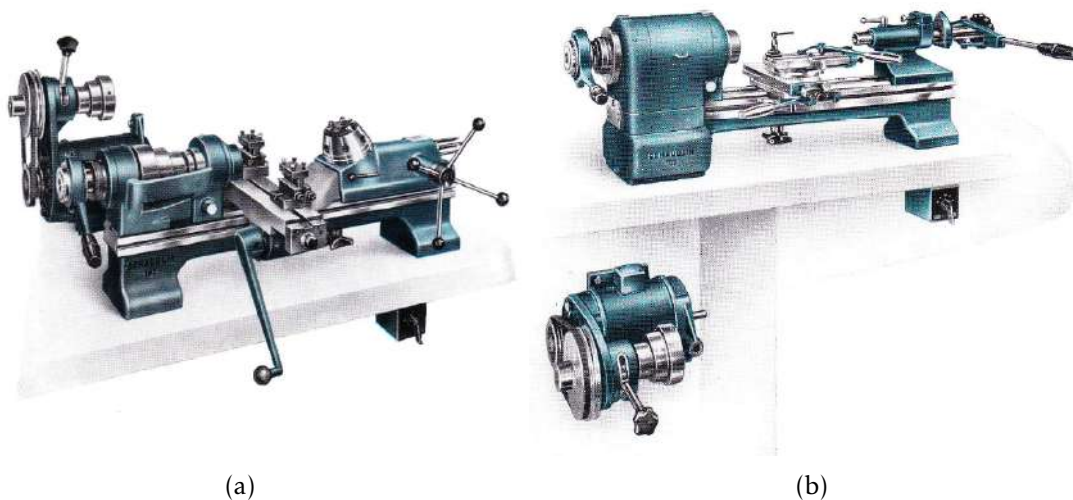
Posições possíveis para instalação do motor: a) Motor instalado lateralmente; b) Motor instalado numa posição inferior; [9].
